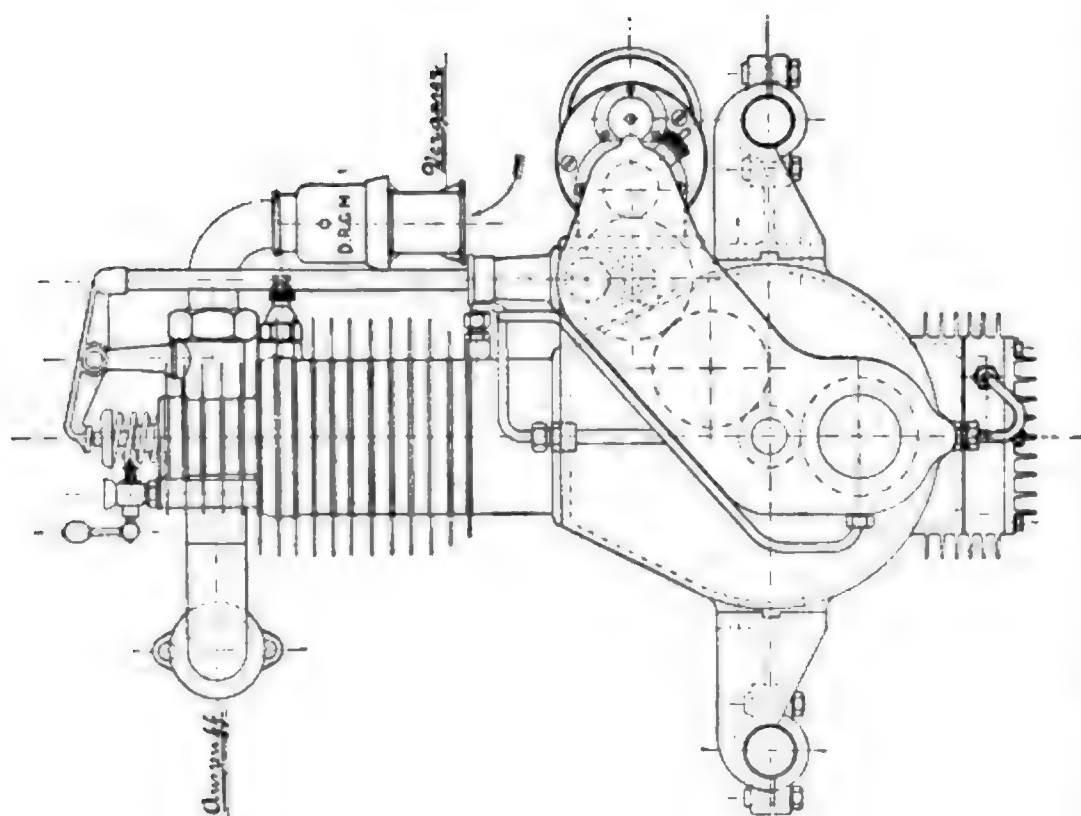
Zeichnung des Flugmotors von Escher & Co., Ansicht von vorn.
